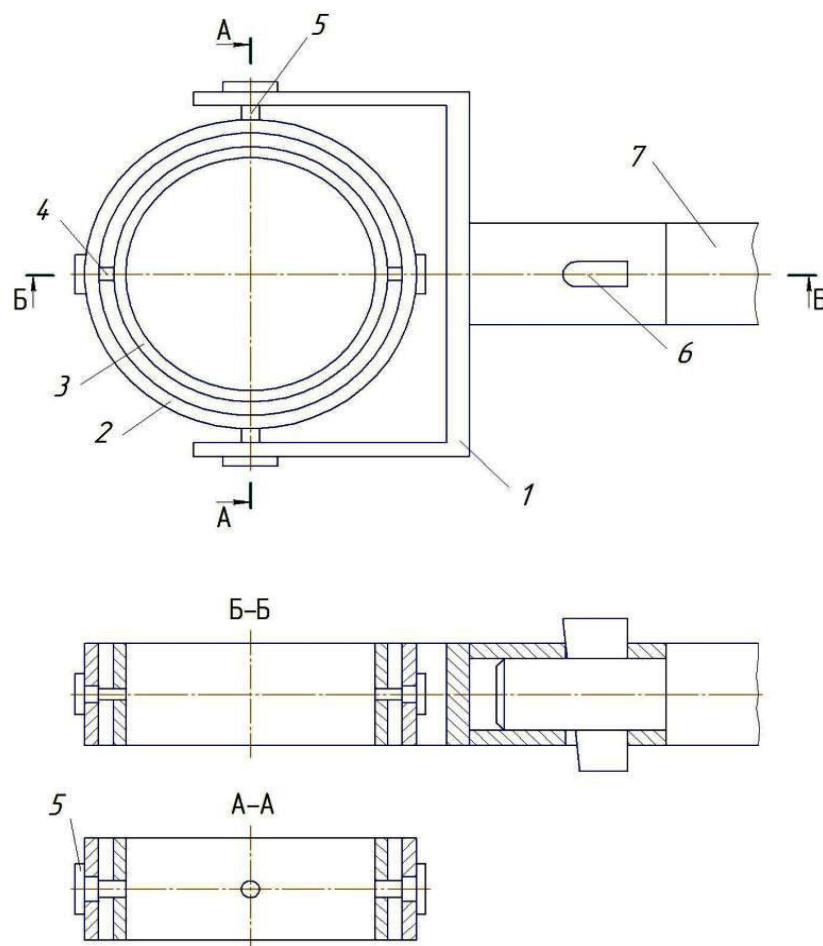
Конструктивное исполнение опорного узла, обеспечивающего самоустановку защитной трубы относительно стакана-коллектора ковшового затвора: 1 – вилка; 2 – наружное несущее кольцо; 3 – внутреннее опорное кольцо; 4 – 5 – цапфы; 6 – штанга; 7 – клин
